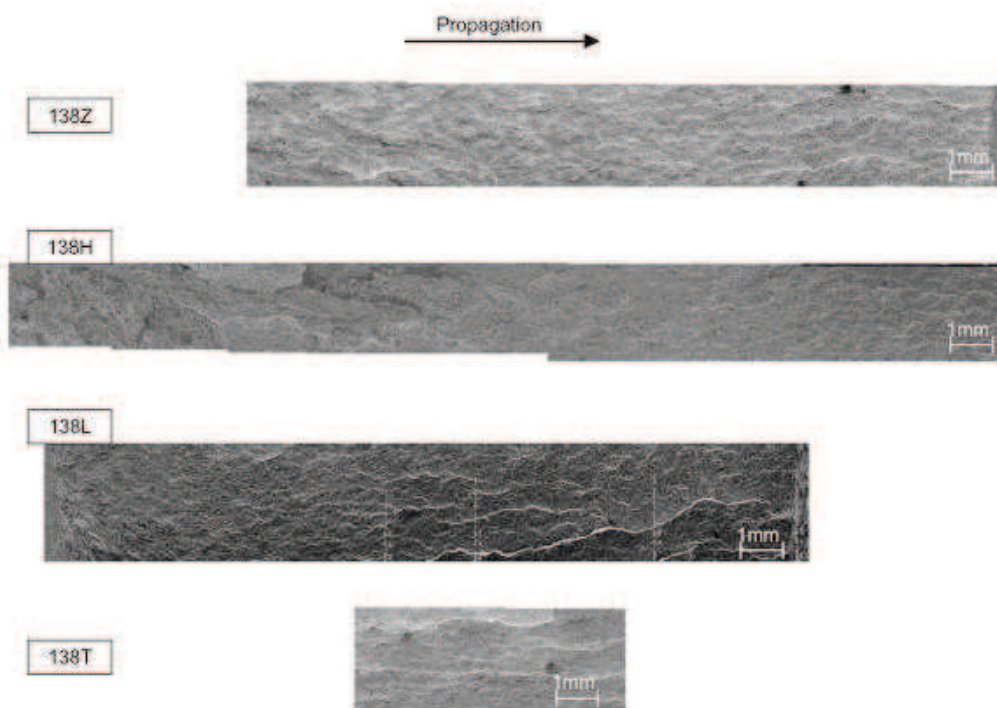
Fractographies des propagations de fissure - éprouvettes CT testées à -125°C
